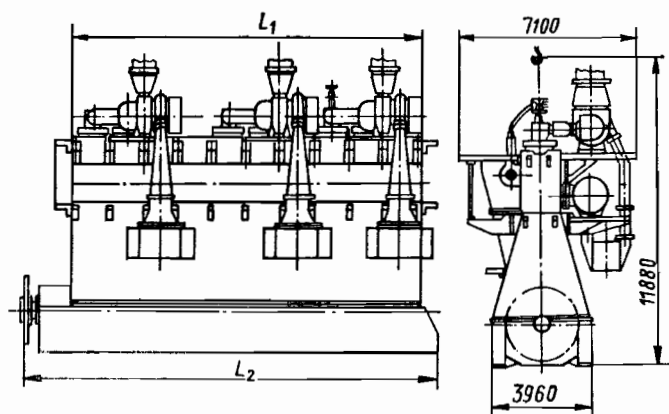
Габаритный чертеж дизеля ДКРН 80/160-4
